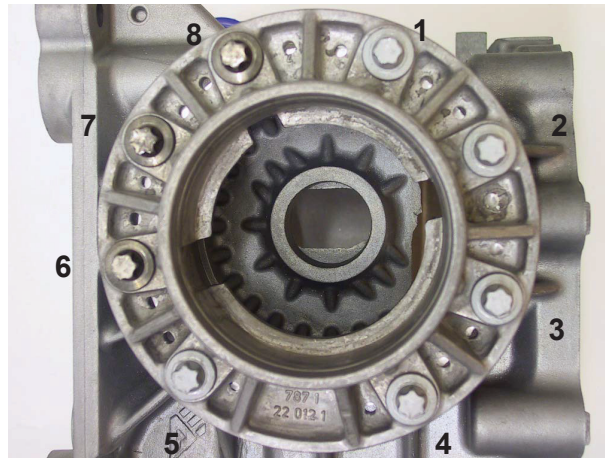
Versuchskörper für galvanische Korrosionsversuche: 8 Schrauben der Legierung EN AW 7075 im Zustand T6 wurden fixiert, Schrauben Nr. 1 - 5 unbeschichtet, Nr. 6 - 8 beschichtet
